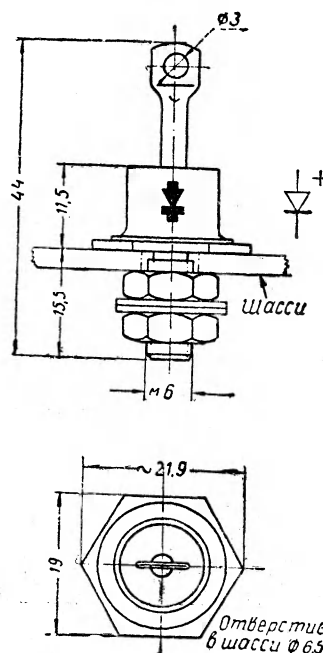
Габаритный чертеж диодов типа Д302—Д305
